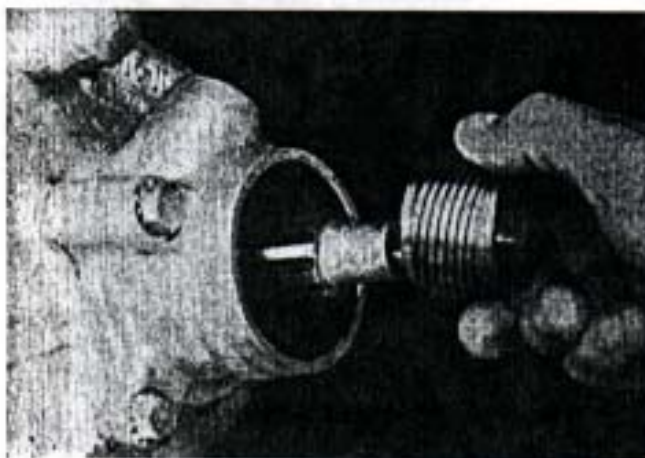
Instalando el engranaje sinfin del velocímetro.
